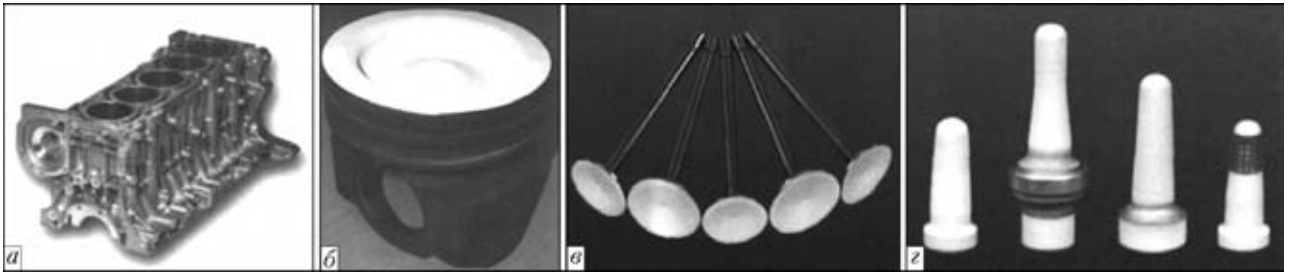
Детали ДВС с ТЗП: а — цилиндры двигателя; б — поршень; в — выпускные клапаны; г — датчики выхлопа и датчики кислорода
